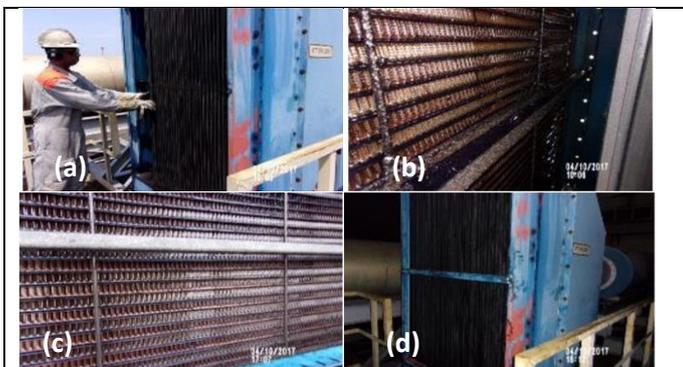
(a) Desmontagem ; (b) inspeção; (c) limpeza; (d) Montagem.
